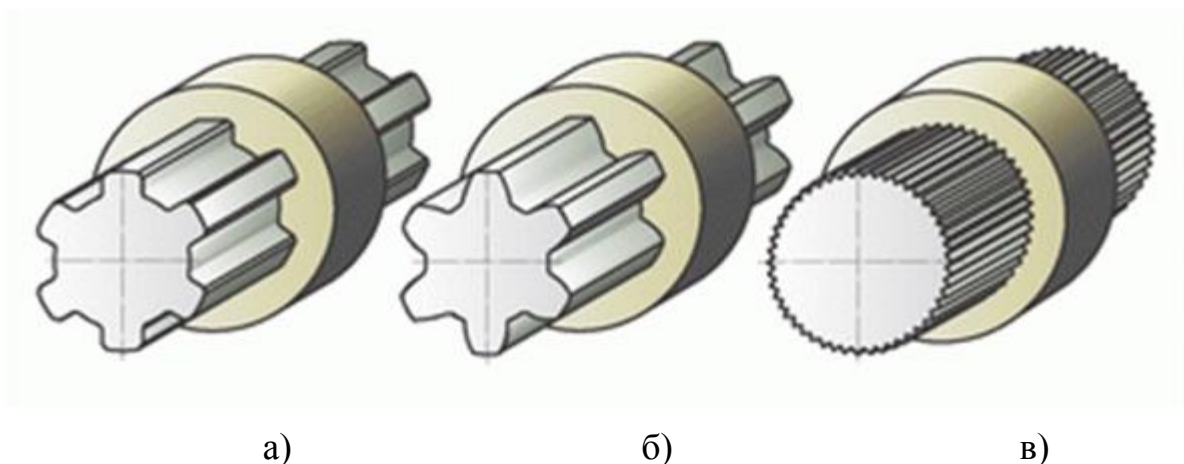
Схема шліцьового з'єднання: а – з прямобокими зубцями, б – з евольвентними зубцями, в – з трикутними зубцями
